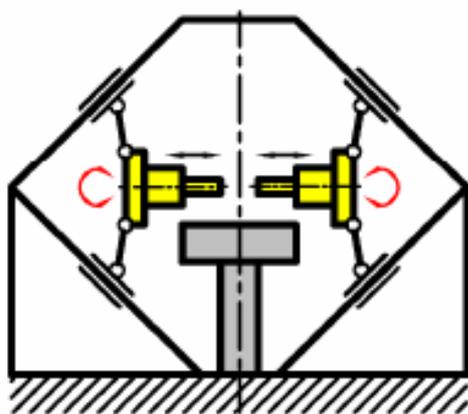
Принципиальная схема станка-робота для обработки зубчатых колес.
